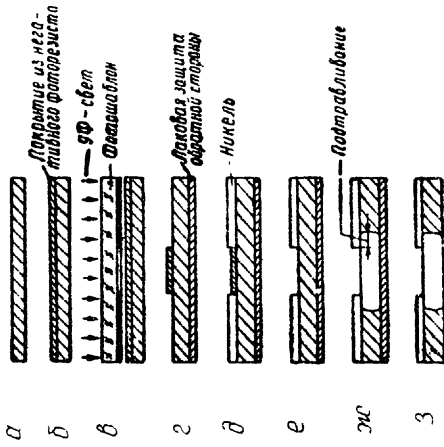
Схема изготовления биметаллических масок: а — подготовка; б — нанесение фоторезиста; в — экспонирование; г — проявление; д — электролитическое нанесение никеля; е — удаление фоторезиста; ж — селективное травление металла; з — готовая маска после удаления лаковой защиты
